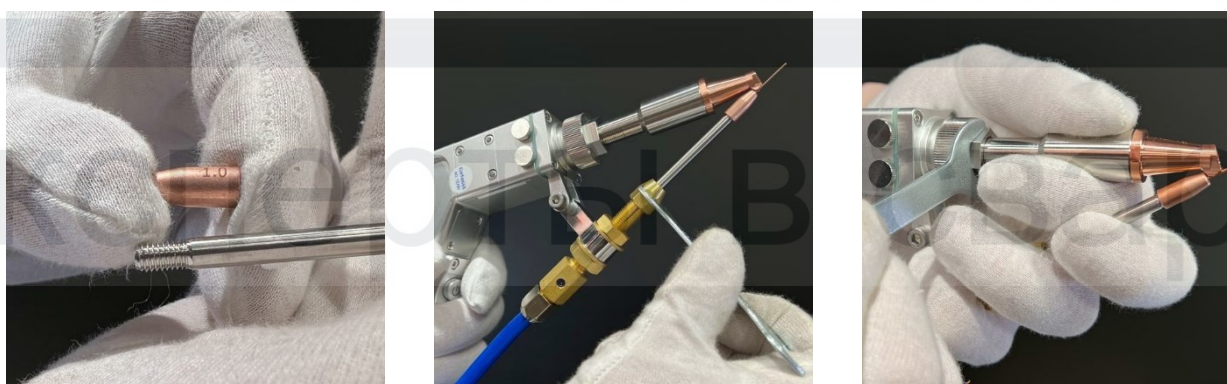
Установка телескопической втулки с наружной резьбой на сварочную головку.
